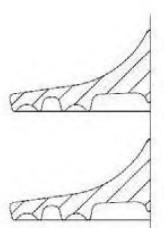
Типичный профиль с мелкими канавками под ребром
